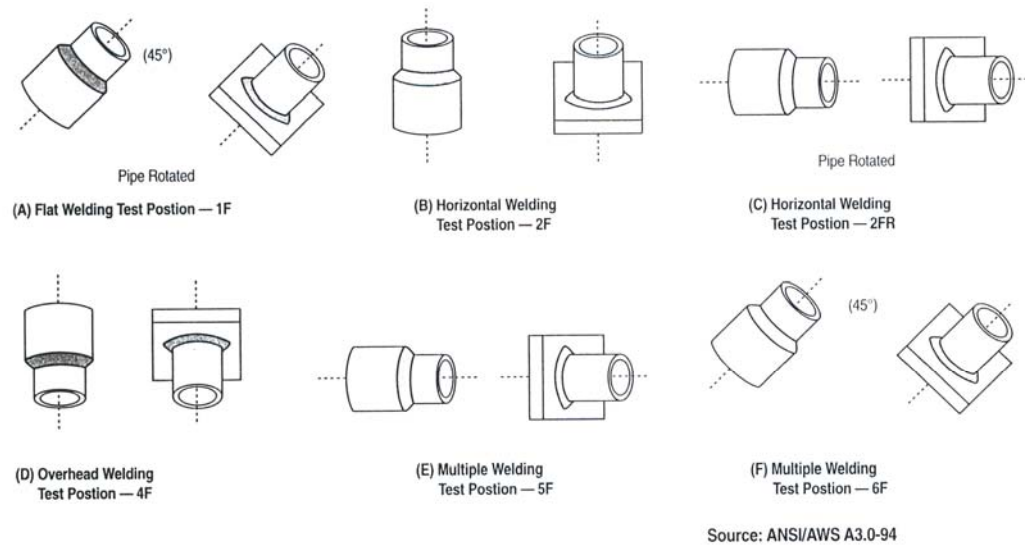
Posiciones de las cañerías de prueba para soldadura de filete.
